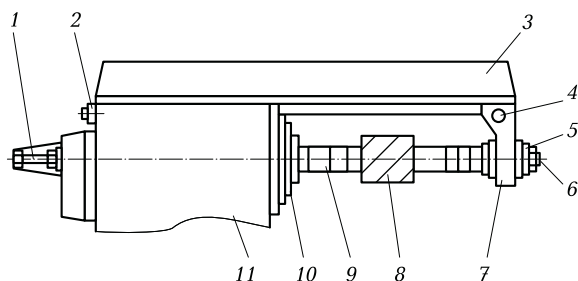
Крепление фрезы на горизонтально-фрезерном консольном станке:
